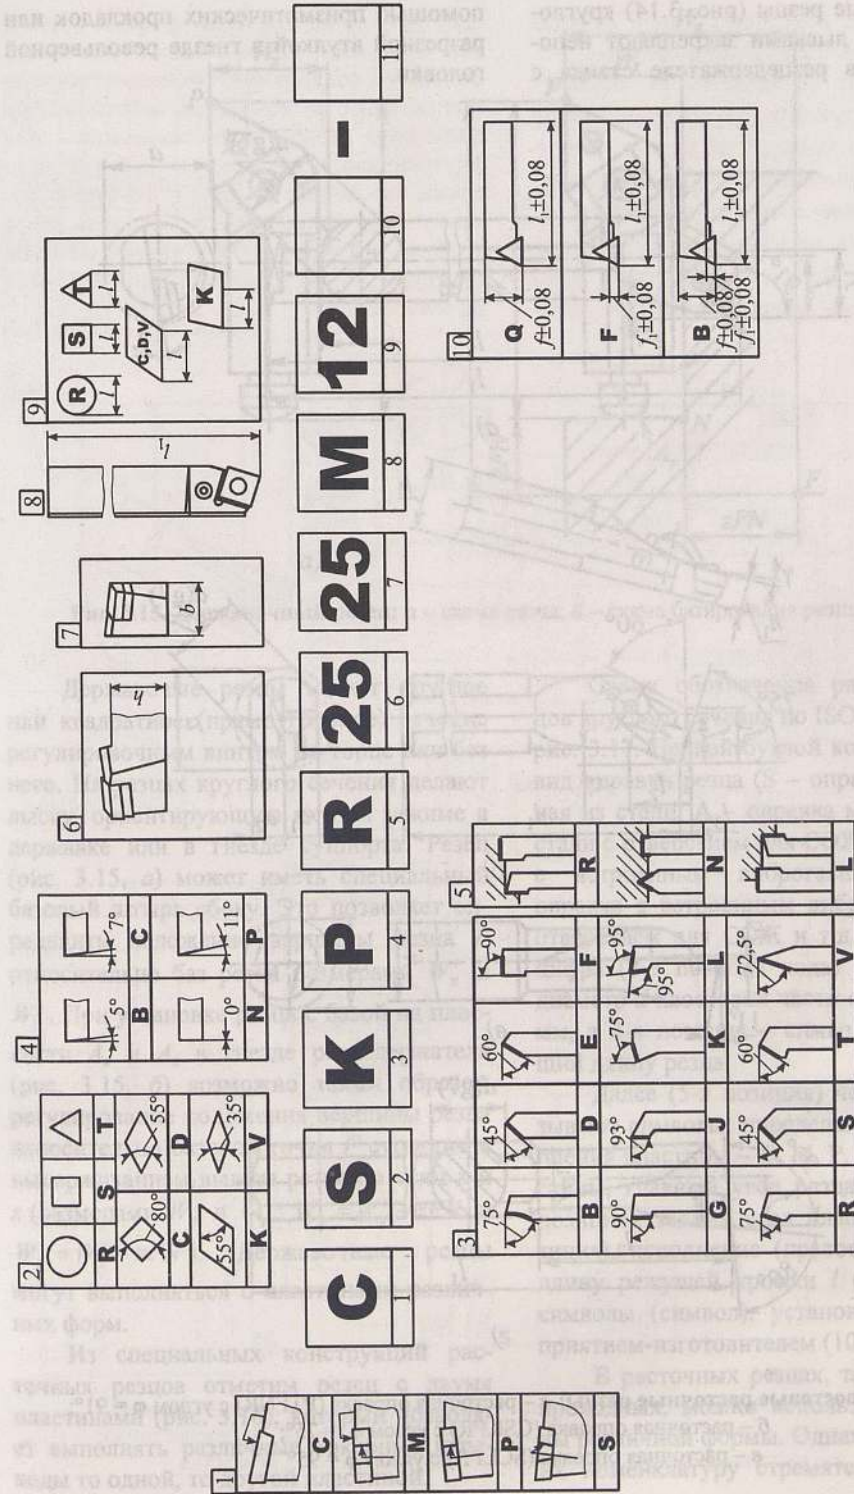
Схема построения обозначений державок токарных резцов для наружного точения по ISO: 1 – метод крепления СМП; 2 – форма СМП; 3 – тип державки по главному углу в плане; 4 – задний угол СМП; 5 – исполнение державки; 6 – высота державки; 7 – ширина державки; 8 – длина резца; 9 – длина режущей кромки; 10 – обозначение для позиционных резцов; 11 – обозначение типа державки заводом-изготовителем
